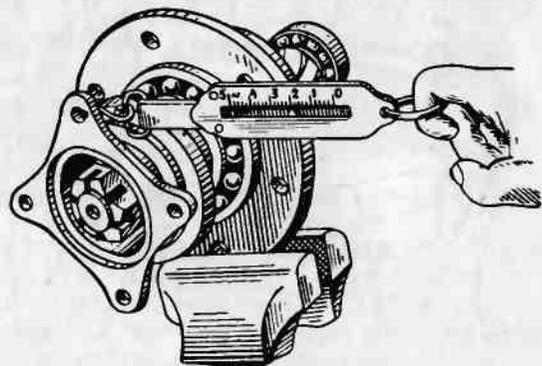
Проверка затяжки подшипников ведущей шестерни главной передачи
